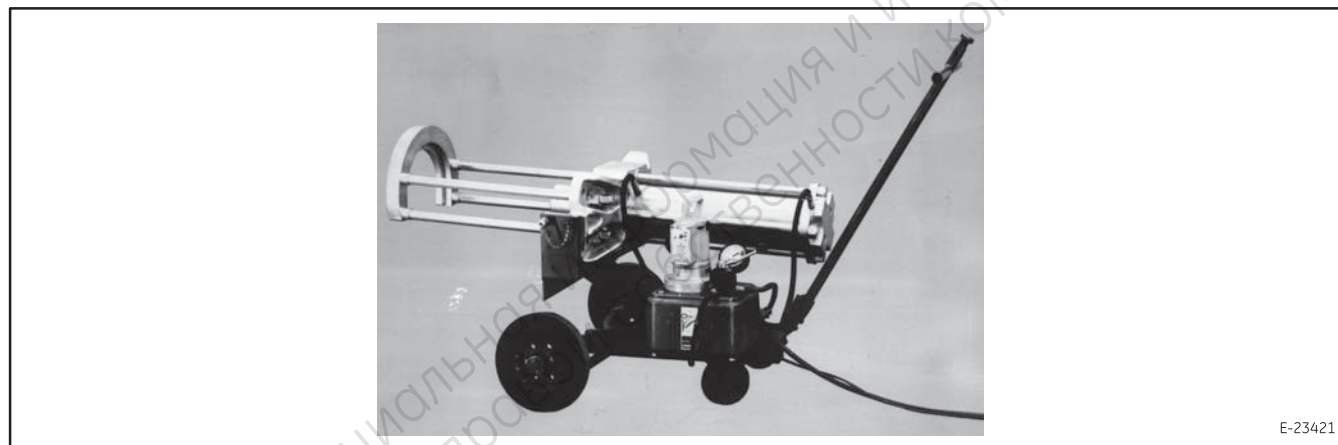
Передвижная установка для распрессовки буксовых подшипников.
